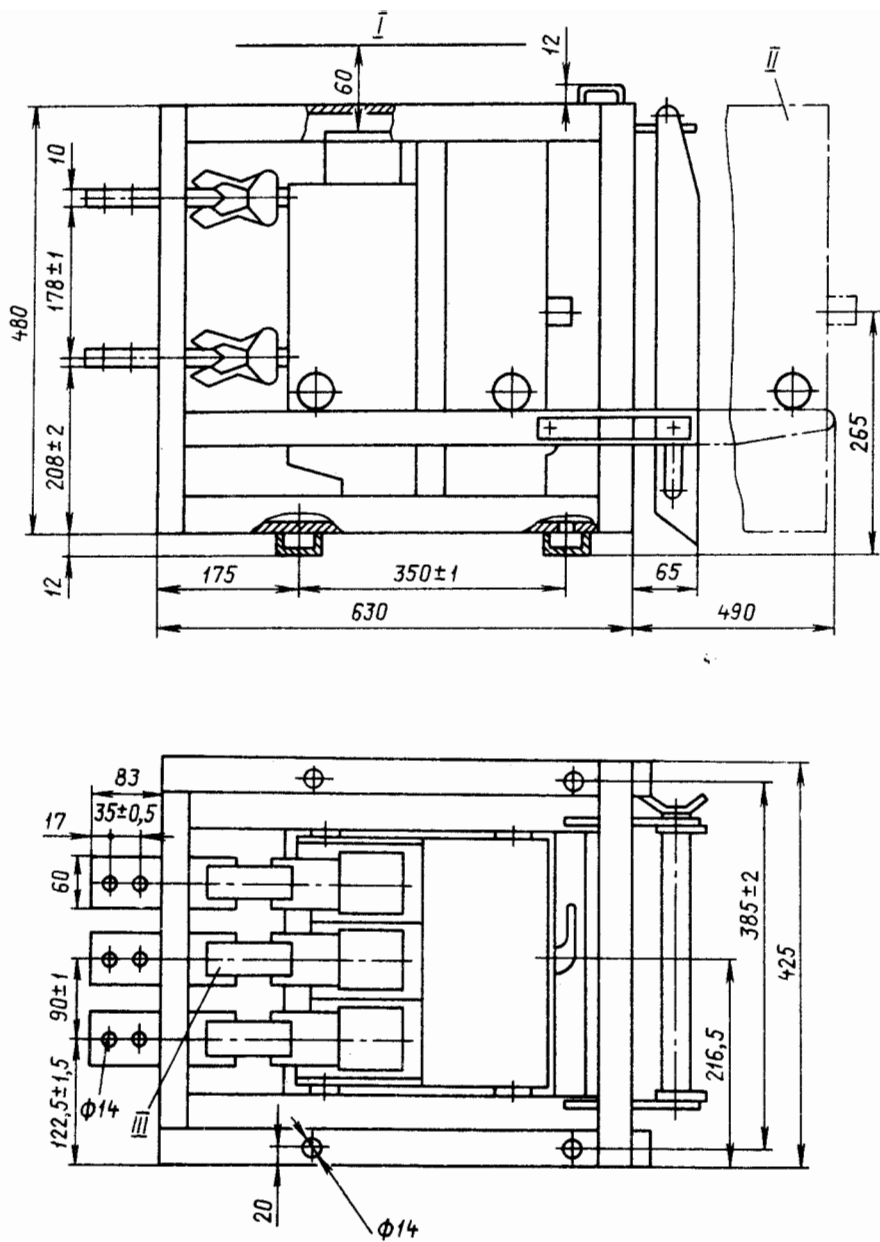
Габаритные и установочные размеры выключателей Э06В в двух- и трехполюсном исполнении:
